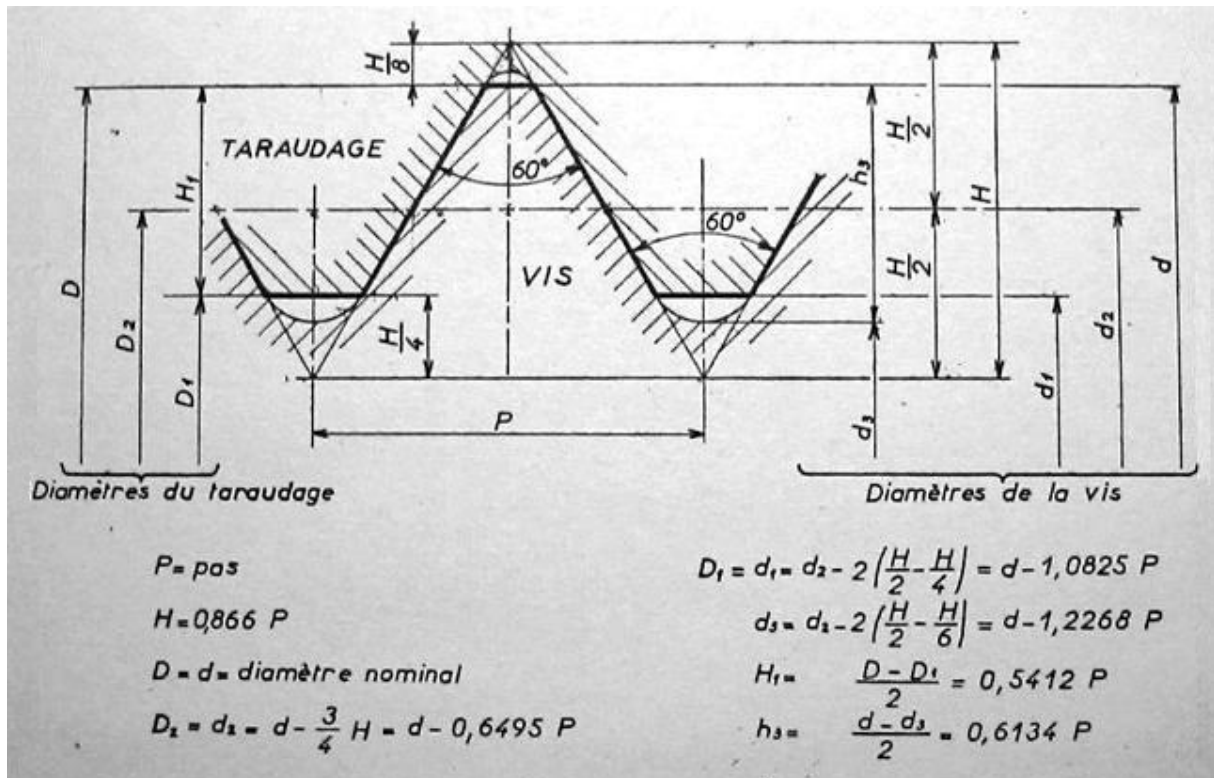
Dimensions normées d'un assemblage fileté vis + écrou selon la norme ISO.
